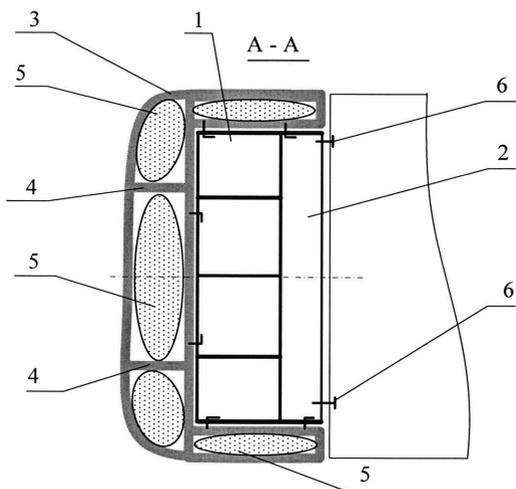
Автомобильный бампер (вид сверху): 1 – несущая балка; 2 – металлический лист; 3 – наружный гибкий корпус; 4 – перегородки; 5 – упругие амортизирующие элементы; 6 – кронштейн
